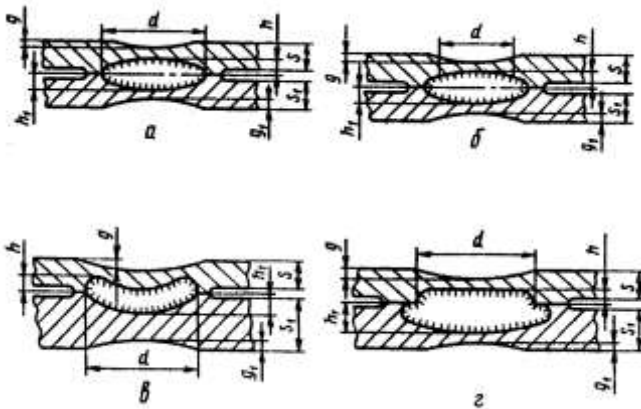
Принципова схема електроконтактного точкового зварювання
